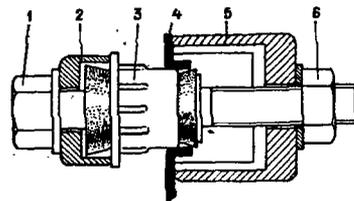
Схема запрессовки шарнира верхнего рычага: 1 - болт; 2 - кольцо приспособления А.47046; 3 - шарнир; 4 - верхний рычаг; 5 - стакан приспособления А.47046; 6 - гайка
